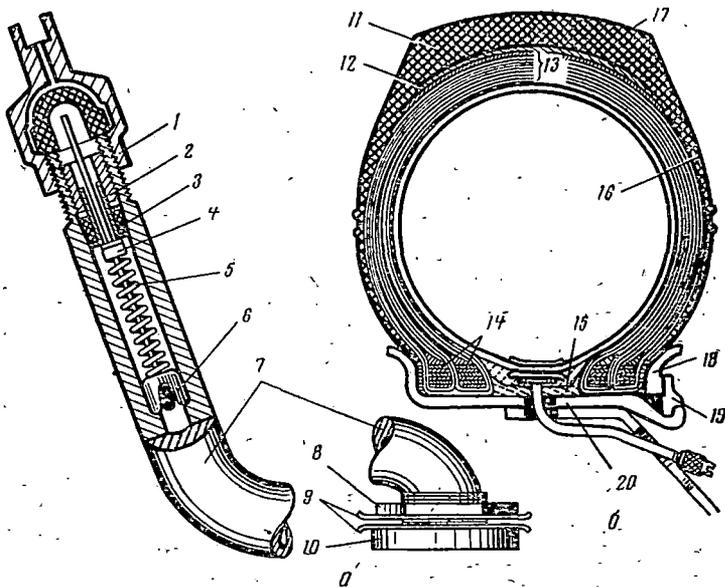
Устройство покрышки шины, обода колеса и металлического вентиля камеры:
